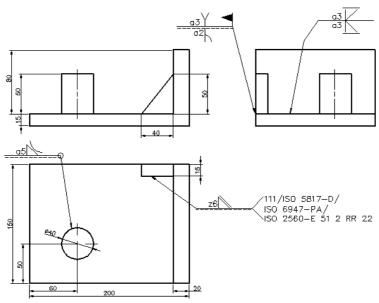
Exemplo de Representação da Juntas Soldadas
